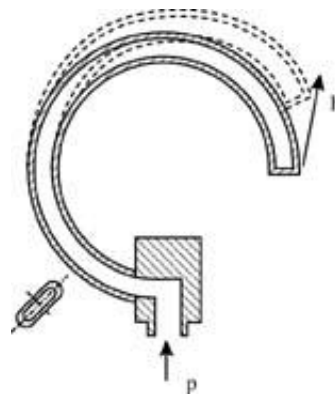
4 – Пружний чутливий елемент – трубчаста пружина
